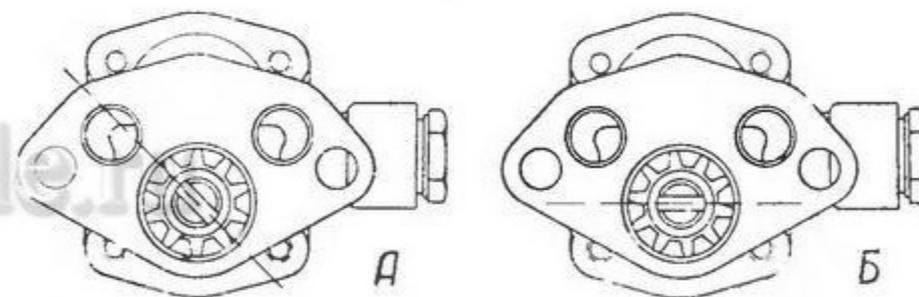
Положение прорези в валике масляного насоса. А—перед установкой на двигатель, Б—после установки на двигатель
